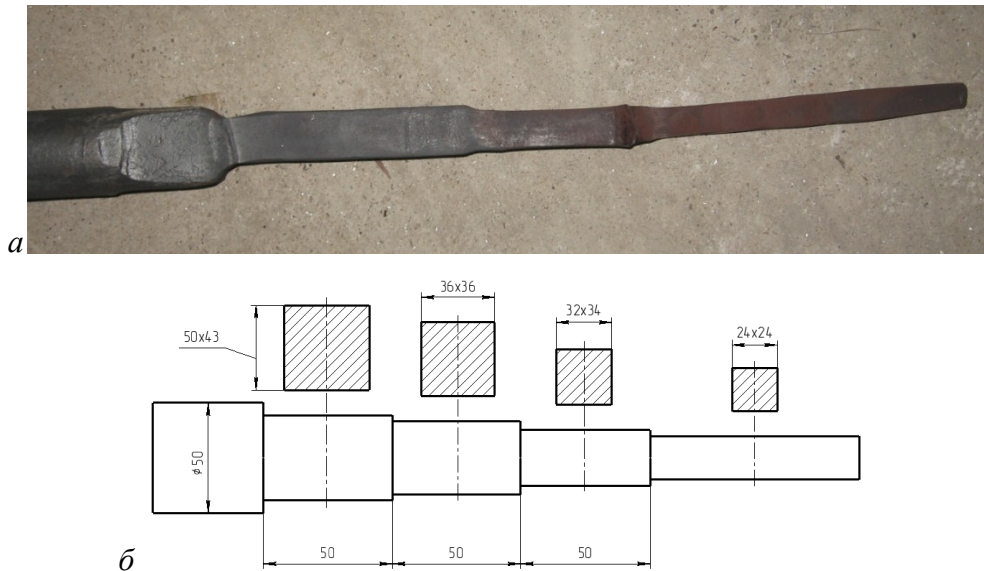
Ступенчатая заготовка: *a* - фотография; *б* - эскиз
